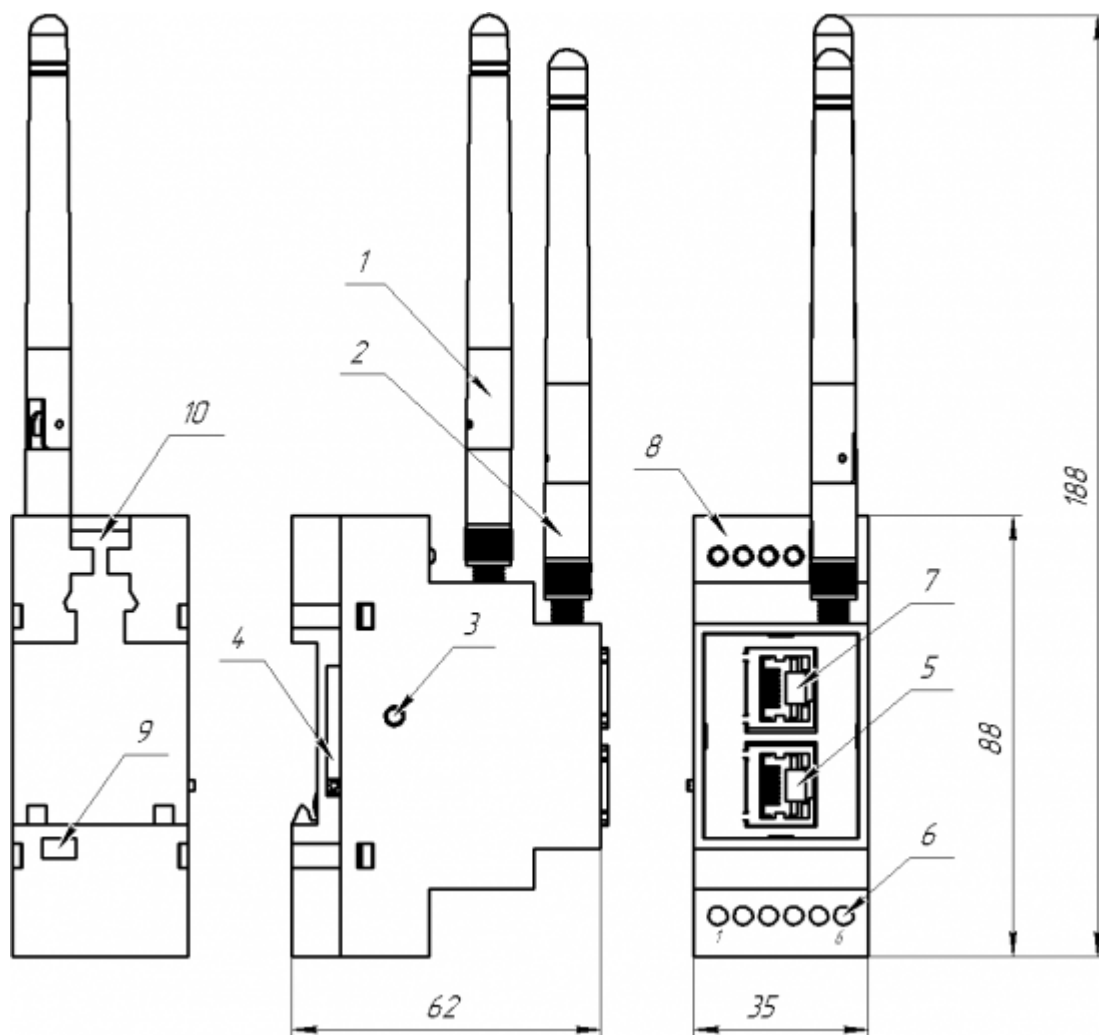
Габаритные размеры и позиционные обозначения СК-01
